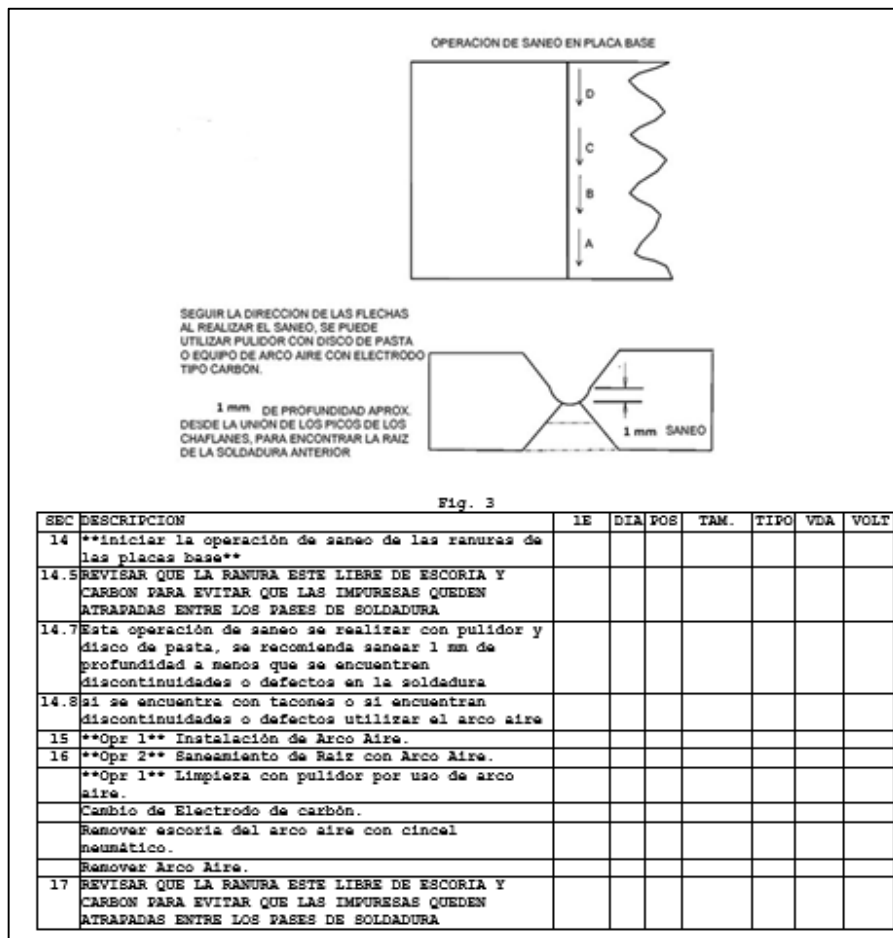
10 Pasos del saneo de soldadura por el segundo lado en la operación de soldadura final de la unión de los pisos (Cortesía de la compañía fabricante de cajas para camión).
